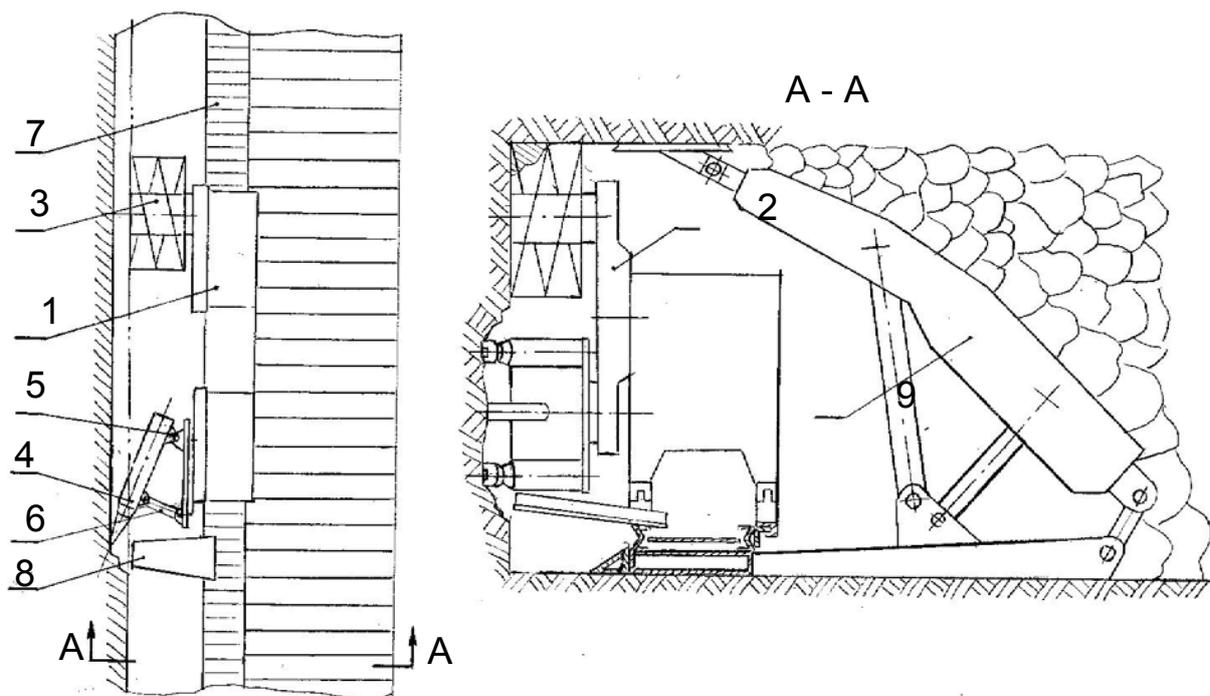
Схема компоновки выемочной машины с режущим и ударным исполнительными органами
